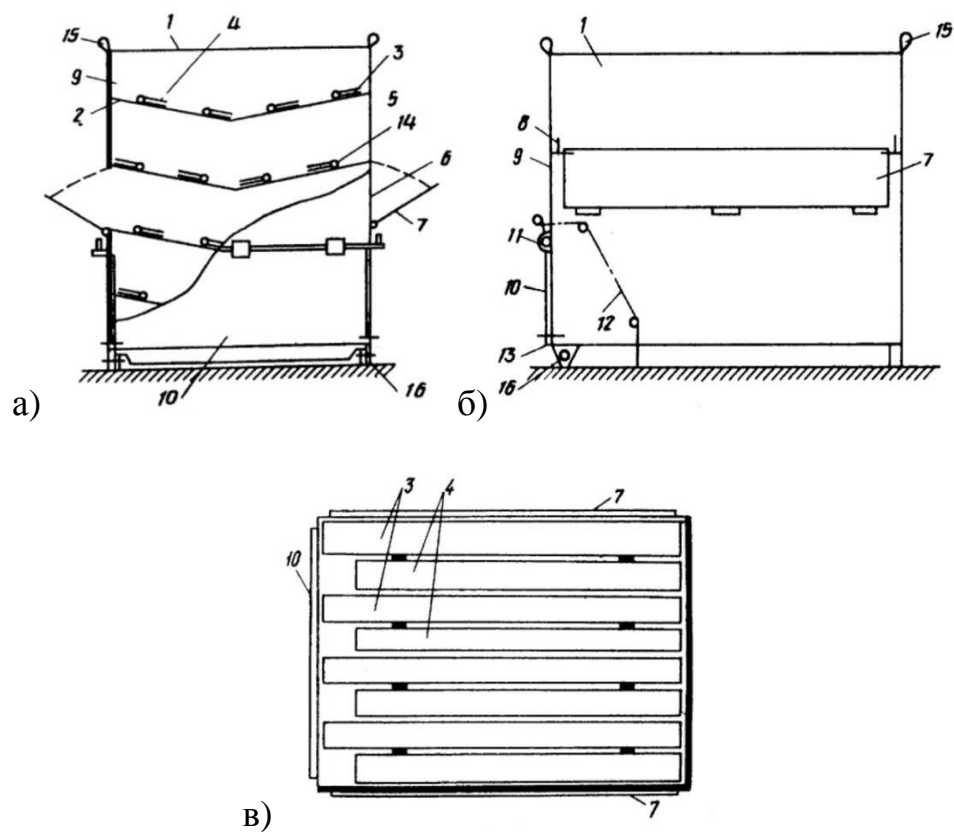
контейнер для перевозки легкоповреждаемых плодов и овощей (А.С. № 1373635): а) вид сбоку; б) вид общий; в) вид сверху с развернутыми шарнирно присоединенными полками. 1 – корпус, 2 – рамки, 3,4 – полки, 5,9 – стенки, 6 – окна, 7 – дверки, 8, 13 – фиксаторы, 10 – створка, 11, 16 – шарнир, 12 – механизм автоматического открывания, 14 – горизонтальная ось, 15 – петли.
